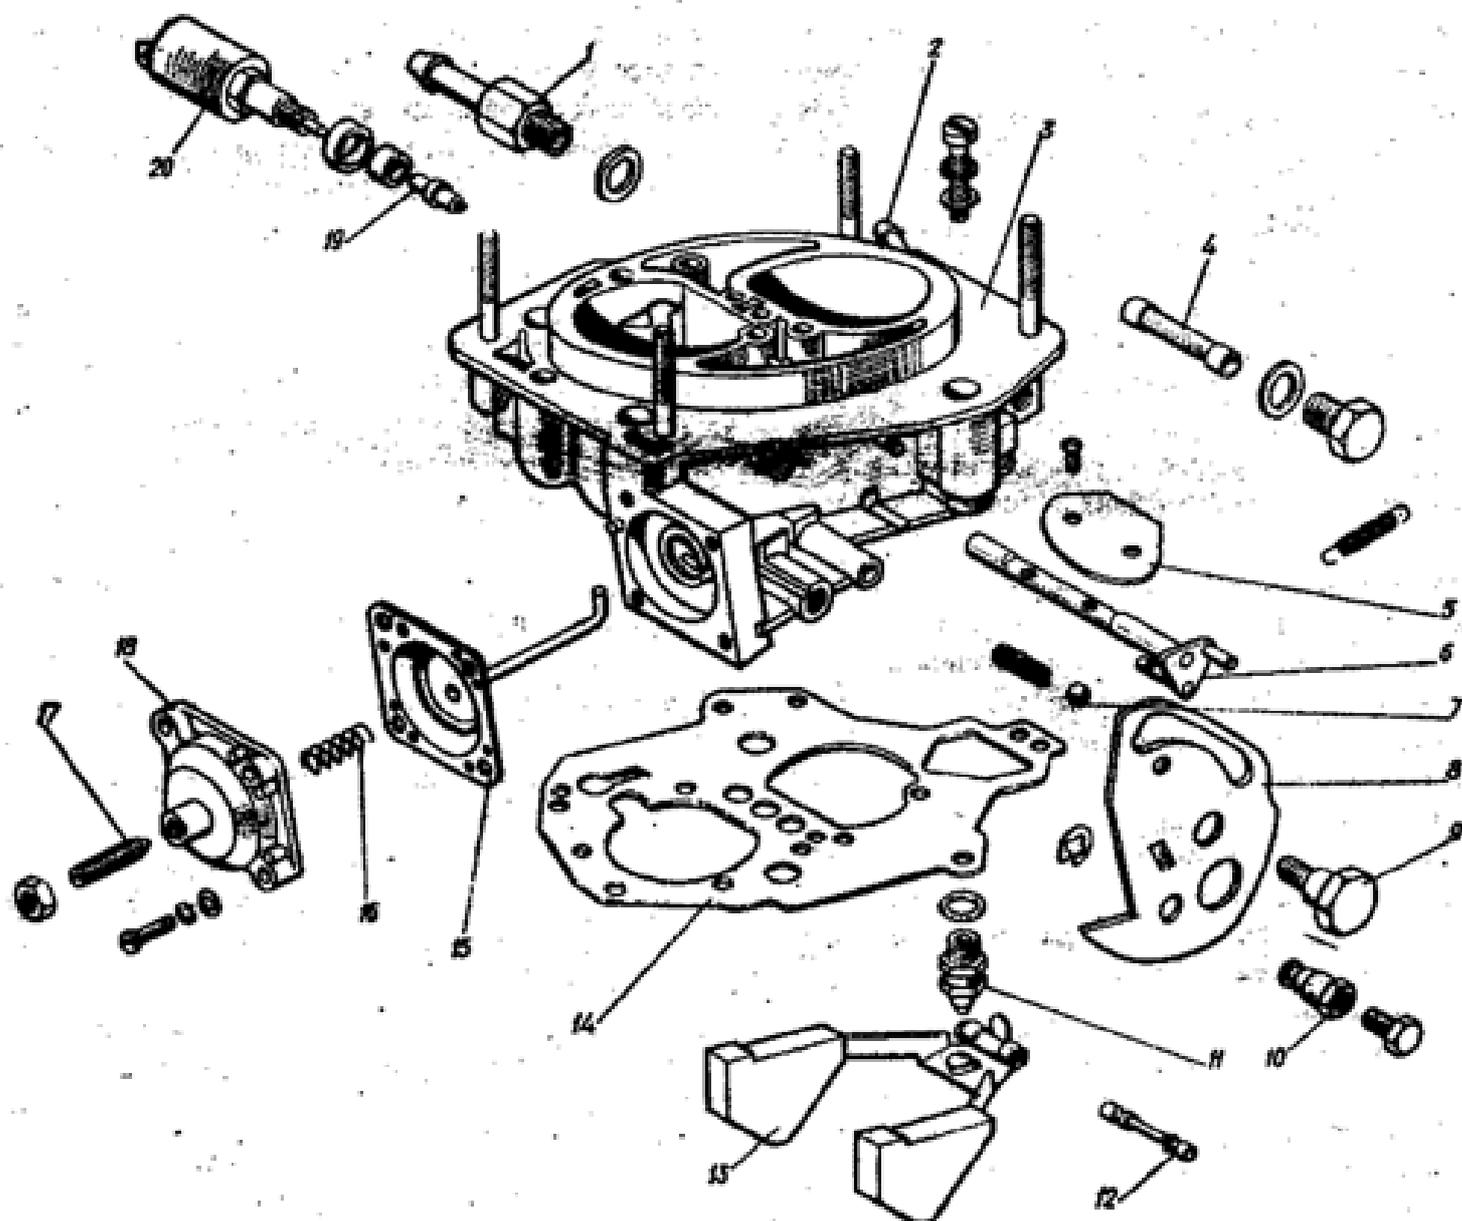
Детали крышки карбюратора: 1 - патрубок подачи топлива; 2 - патрубок слива топлива; 3 - крышки карбюратора; 4 - топливный фильтр; 5 - воздушная заслонка; 6 - ось воздушной заслонки с рычагом; 7 - шарик фиксации рычага управления воздушной заслонкой; 8 - рычаг управления воздушной заслонкой; 9 - ось рычага; 10 - втулка крепления тяги привода воздушной заслонки; 11 - игольчатый клапан; 12 - ось поплавка; 13 - поплавок; 14 - прокладка; 15 - диафрагма пускового устройства со штоком; 16 - пружина; 17 - регулировочный винт; 18 - крышка пускового устройства; 19 - топливный жиклер холостого хода; 20 - электромагнитный запорный клапан.
